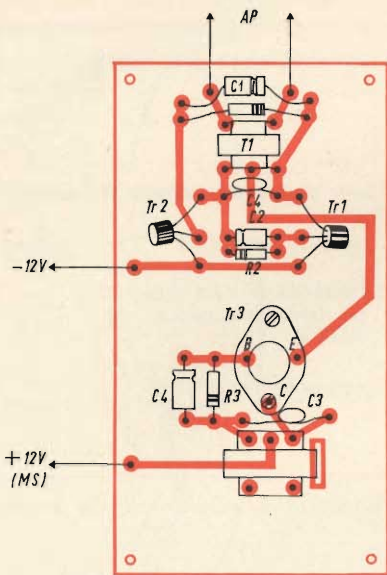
Serigrafia del circuito stampato e vista dei componenti montati sopra un unico chassis.
